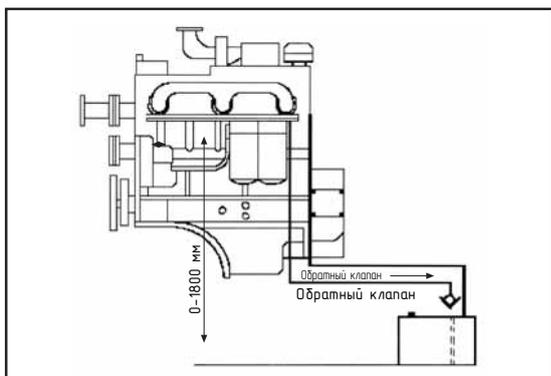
Стандартная схема подачи топлива с баком ниже отметки двигателя
